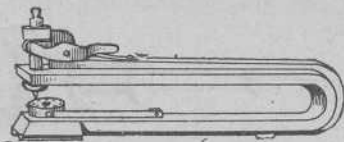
Agujereadora, llamada revólver, para piezas pequeñas.
